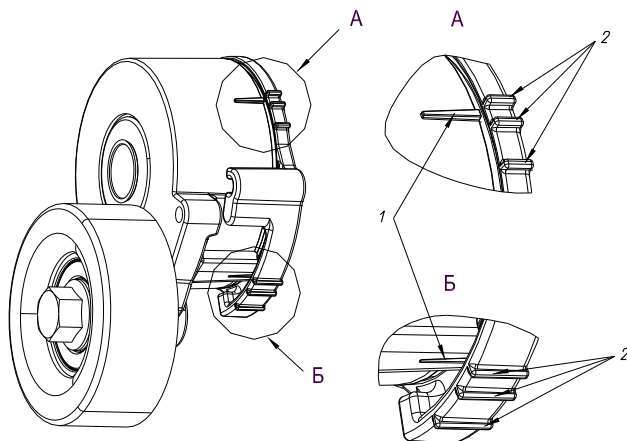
Контроль за натяжением ремней привода агрегатов:
